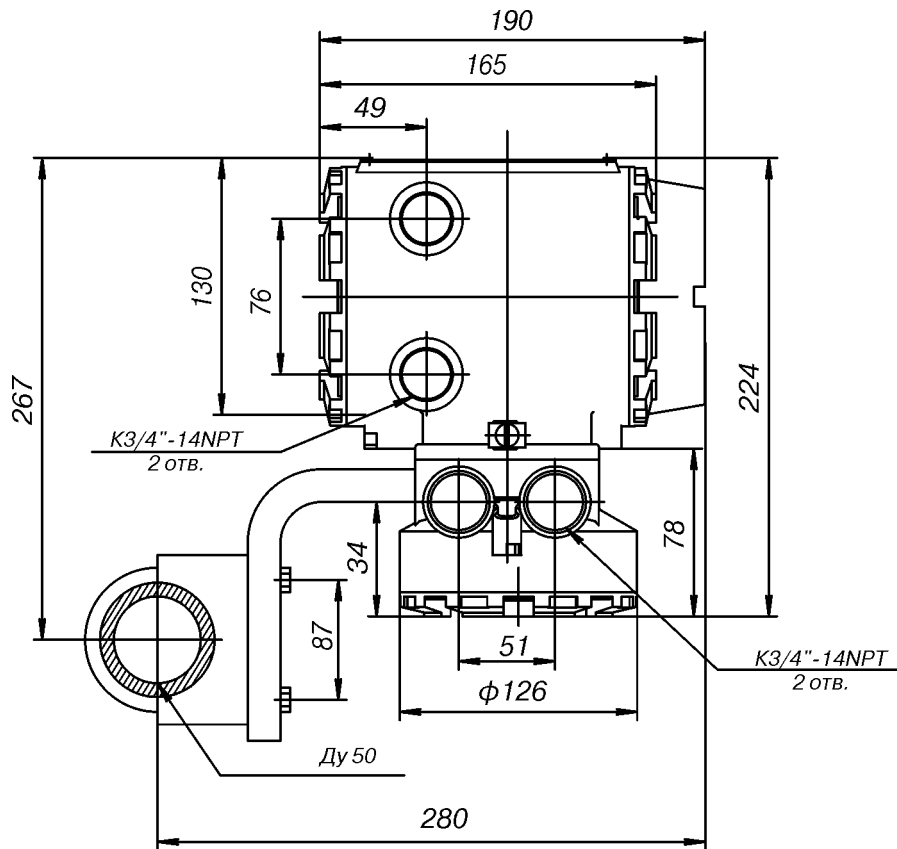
Габаритные и присоединительные размеры преобразователя 8732C (удаленный монтаж на трубе Ду 50 мм).
